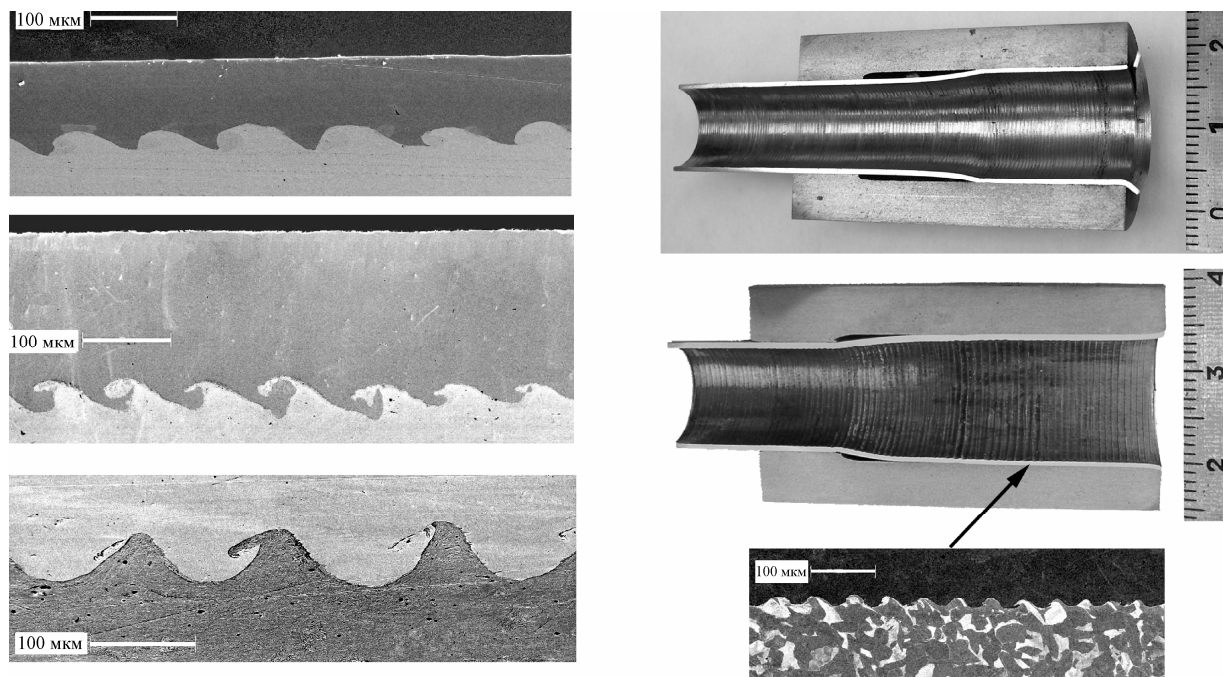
Примеры использования эмульсионных ВВ для сварки взрывом.
